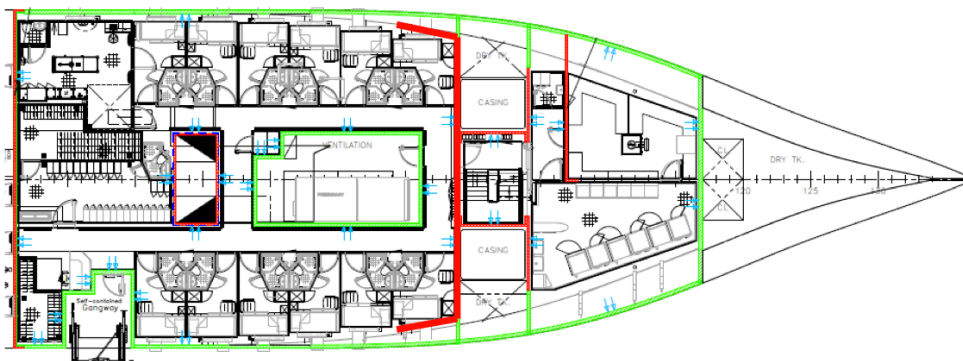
Aislamiento de la cubierta principal: mamparos.
